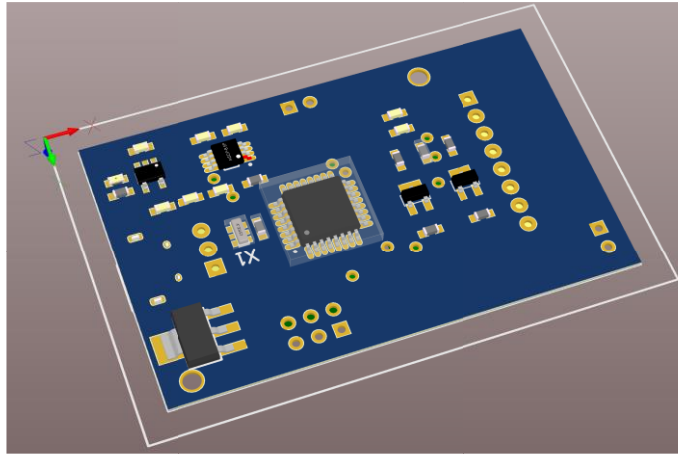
Resultado del PCB Final en perspectiva visto desde la Capa Inferior [20]
